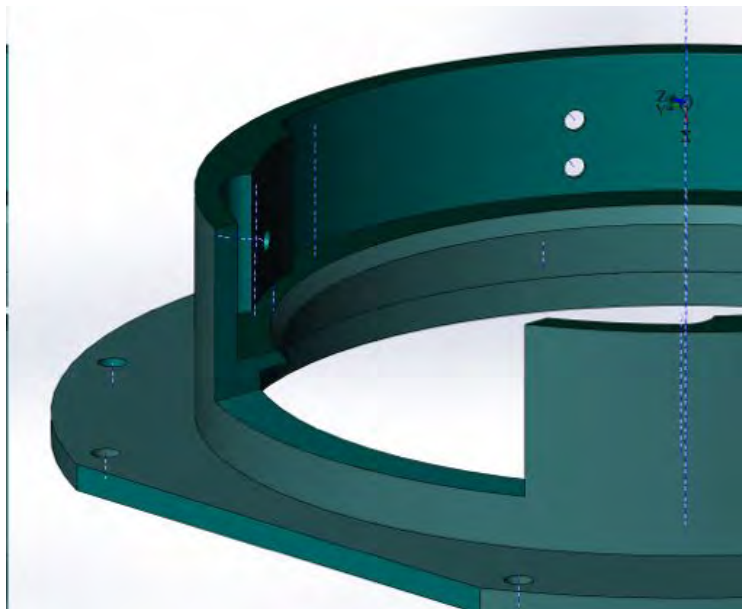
Detalle de maquinado extra único para la Celda cámara roja C1.
